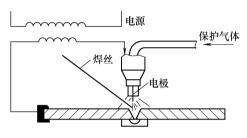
非熔化极气体保护焊的焊接过程
